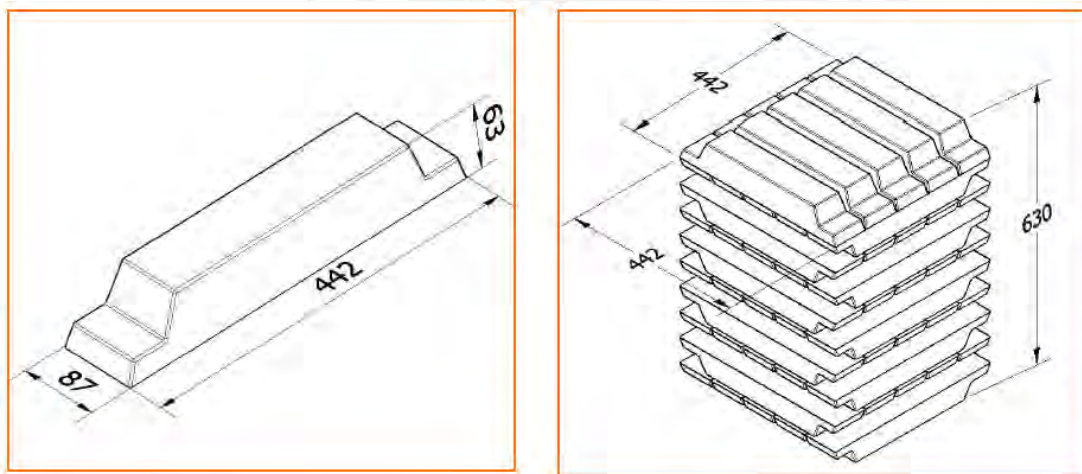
Disposición de baterías en un paquete (dimensiones en mm)
